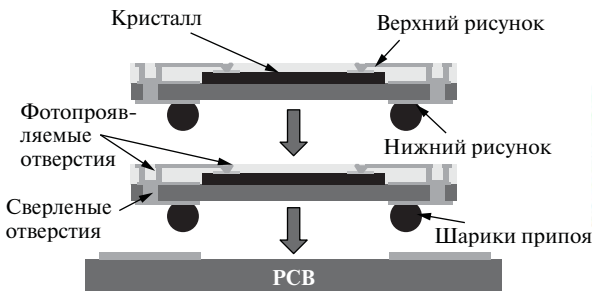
Двухэтажная сборка кристаллов или микрокорпусов
